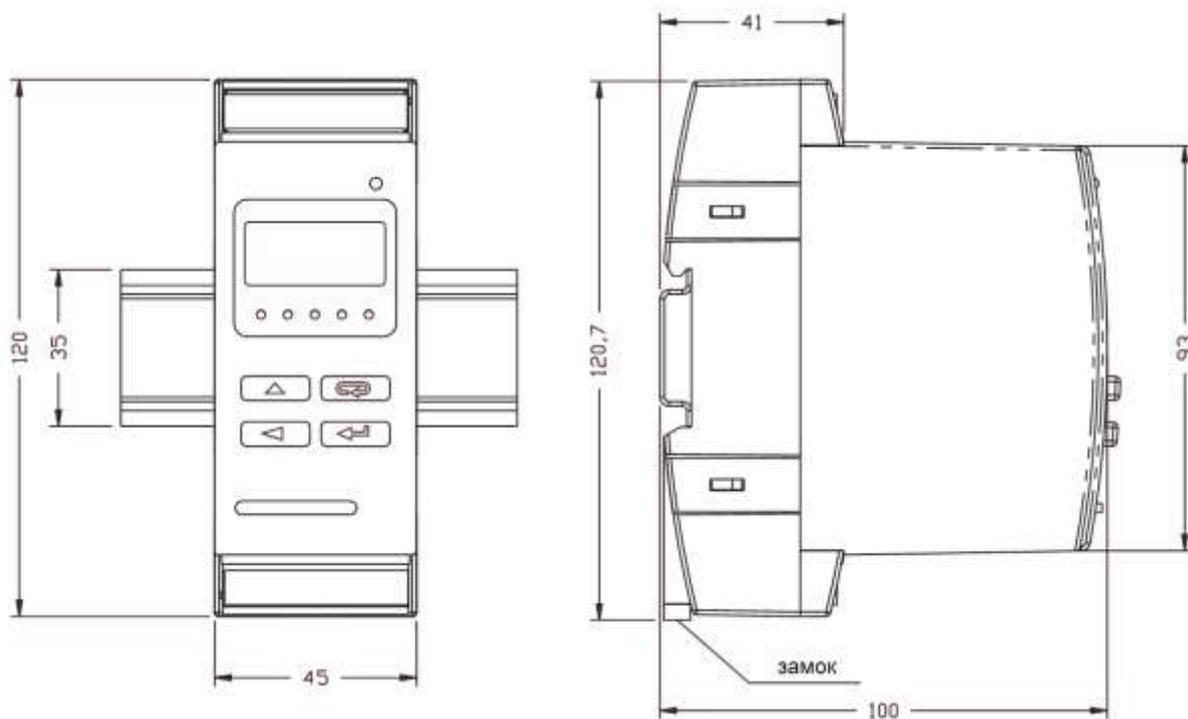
Габаритные размеры и способ крепления преобразователя Р300
